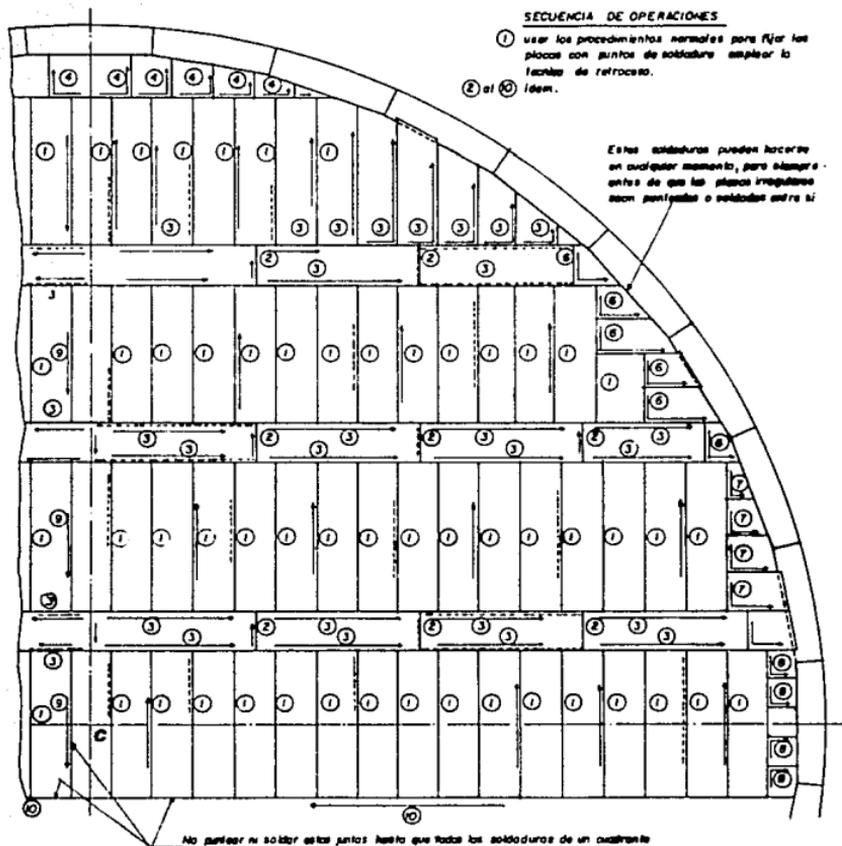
Secuencia de Soldeo en Placas de Fondo
